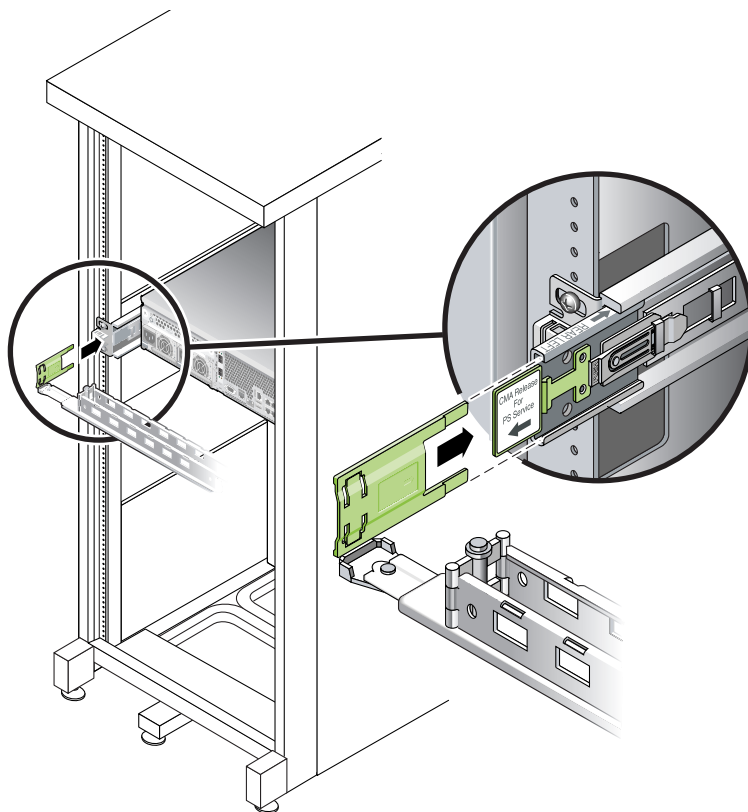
Montaje del lado izquierdo de la guía deslizante
